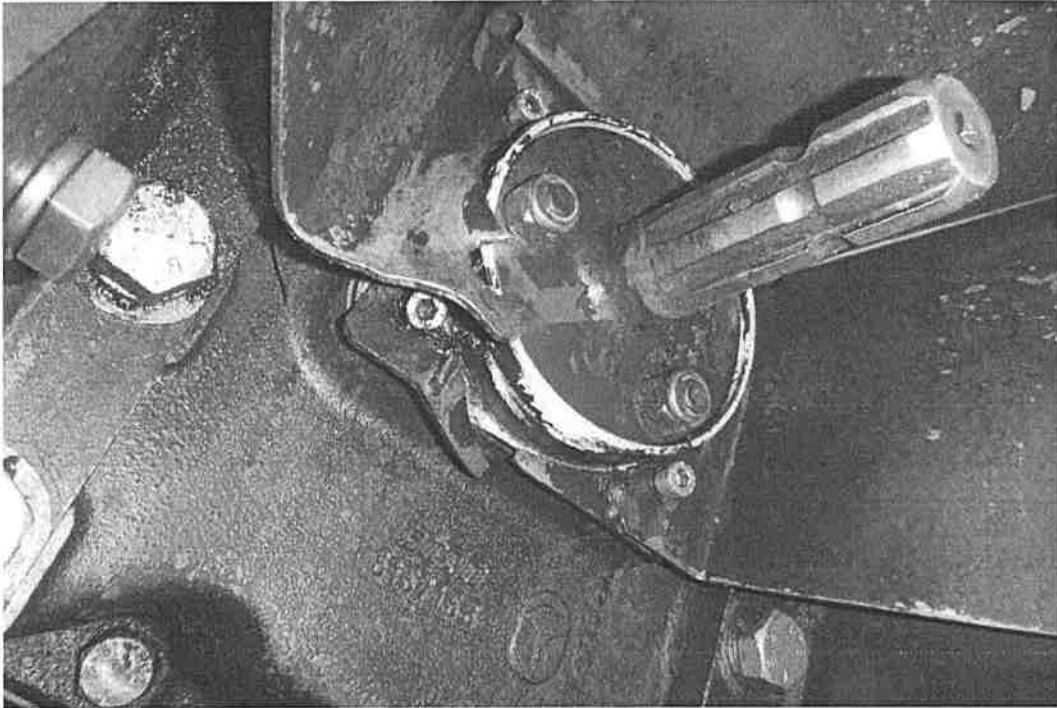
Autre vue rapprochée de la photo précédente, montrant d'autres traces d'endommagement sur le boîtier métallique protecteur de la prise de force arrière.
